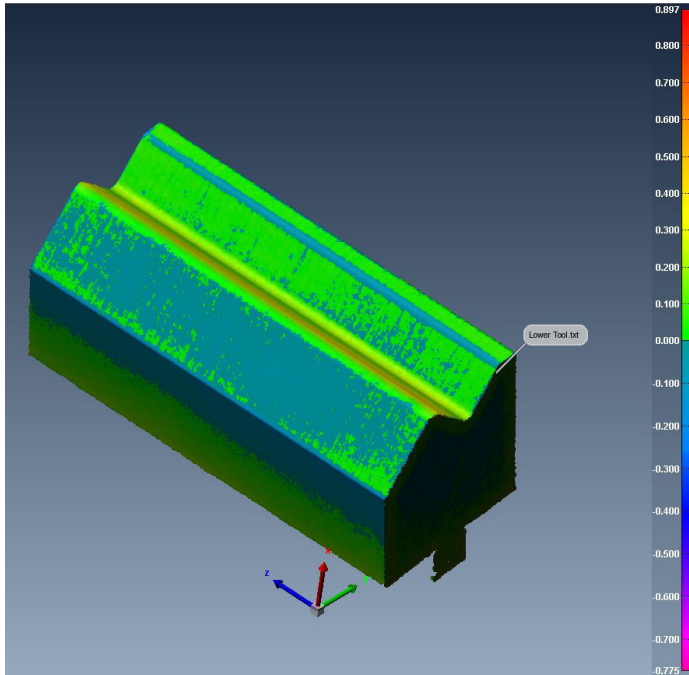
3D-Scan eines gedruckten Werkzeugs
